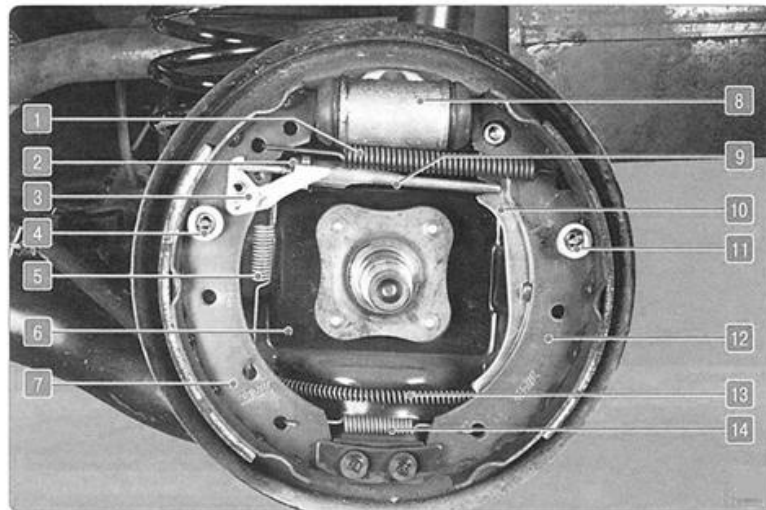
Гальмівний механізм заднього колеса: 1 – верхня стяжна пружина; 2 – регулятор зазорів; 3 – важіль регулятора; 4, 11 – опорні стійки («солдатики»); 5 – пружина важеля; 6 – гальмівний щит; 7 – передня колодка; 8 – робочий колісний циліндр; 9 – розпірна планка; 10 – розтискний важіль стоянкового гальма; 12 – задня колодка; 13 – трос стоянкового гальма; 14 – нижня стяжна пружина.
